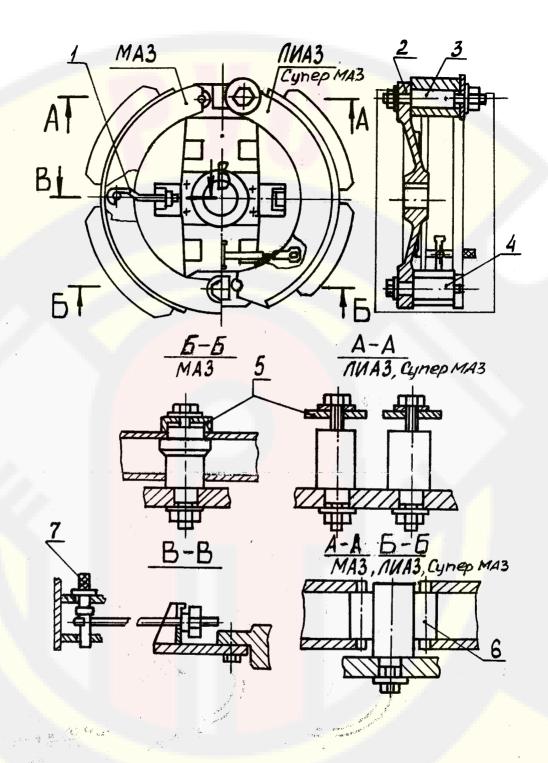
Приспособление для обточки тормозных накладок автомобилей МАЗ. ЛиАЗ, Супер МАЗ
